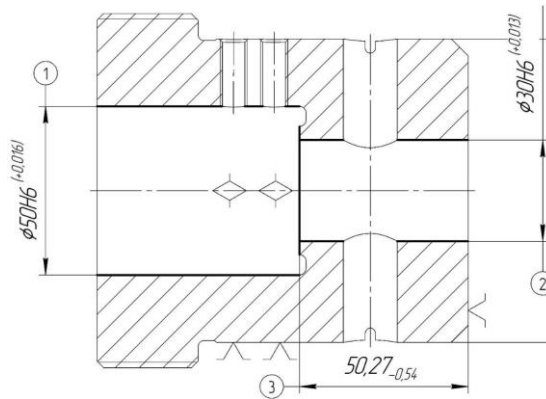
Схема базування деталі в гідропластовому патроні
